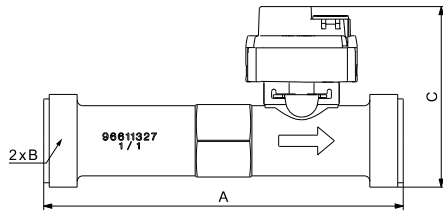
Abmessungen des Sensors MFS 10-100 l/min (ohne Adapter)
